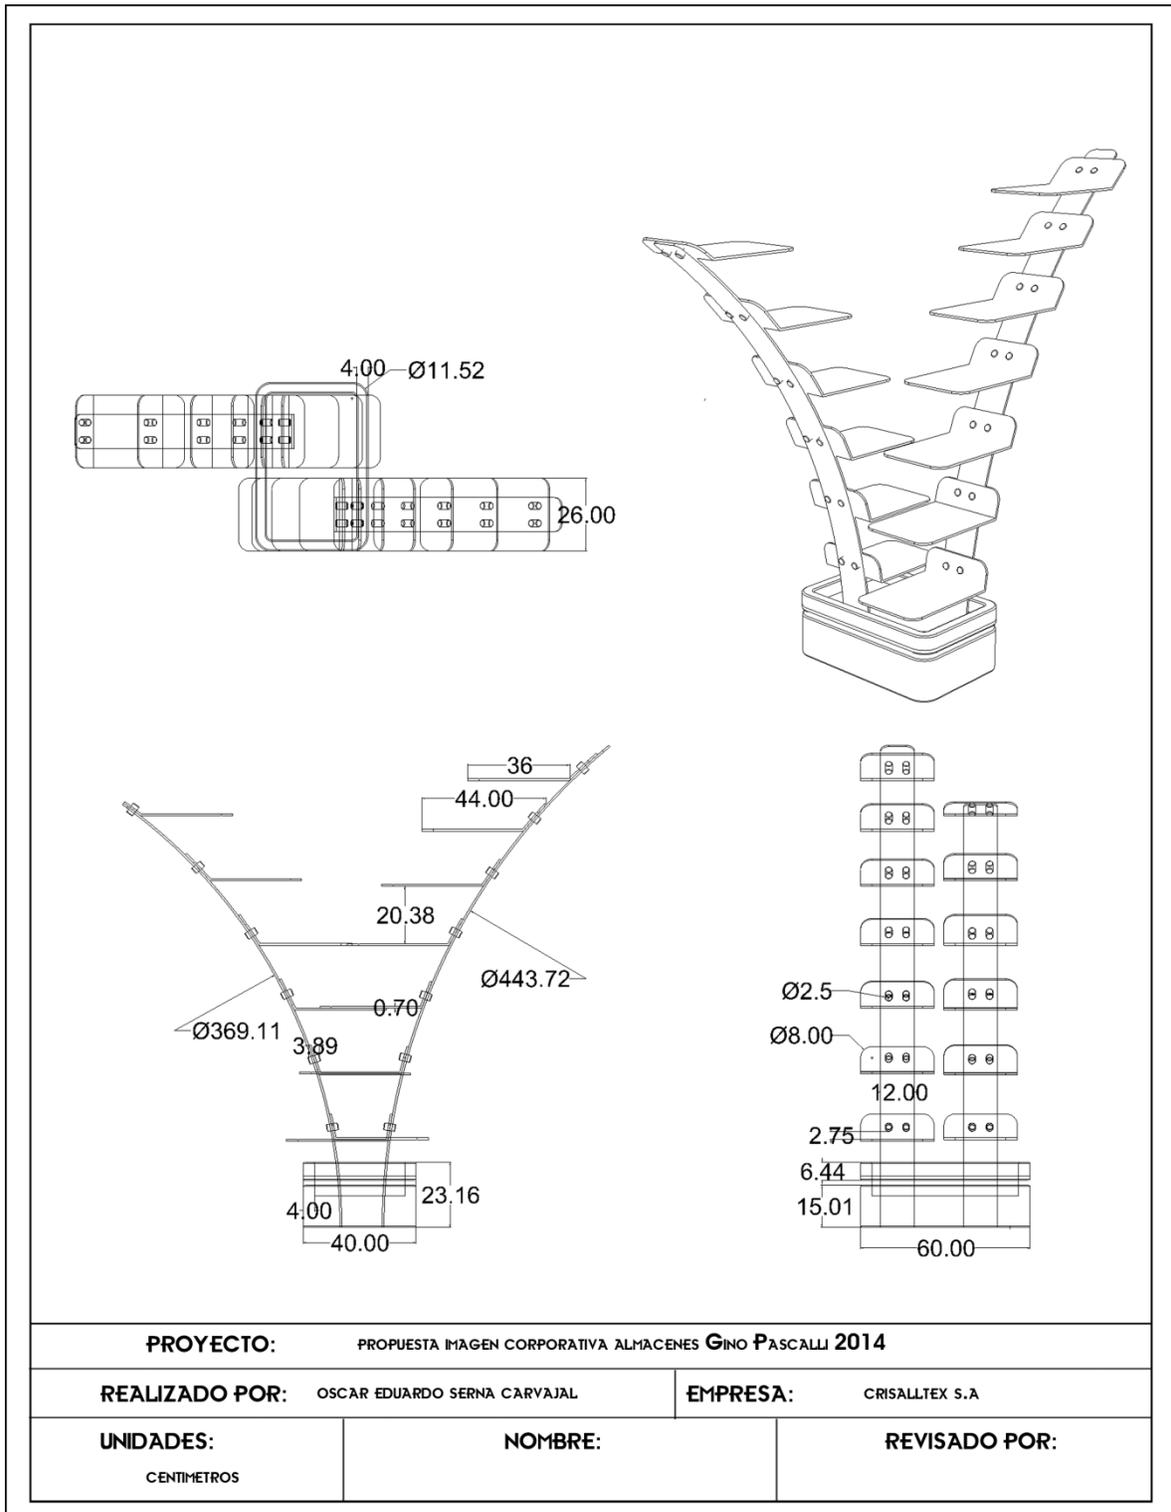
Planos Técnicos Exhibidor Móvil Calzado
